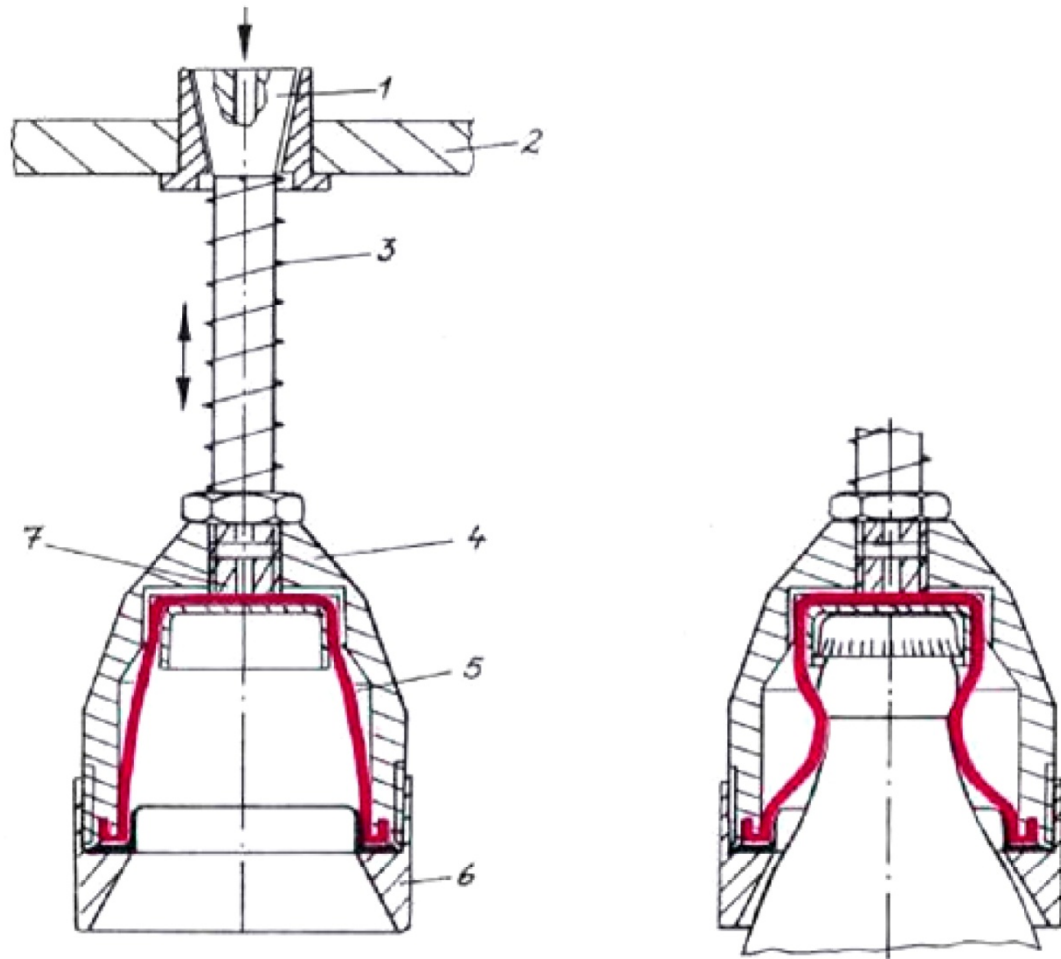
Пневматичний захватний патрон: 1 – напрямний конус, 2 – захватна головка, 3- гвинтова пружина, 4 – корпус захватного патрона, 5 – еластична манжета, 6 – гайка, 7 – гвинт
